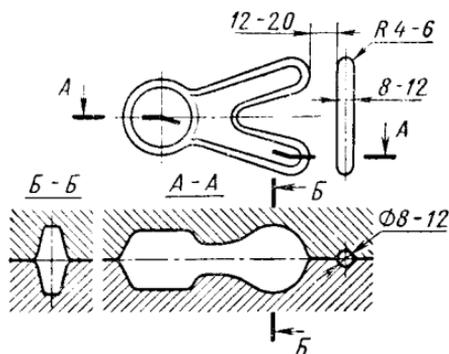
Канавка для торможения заусенца у предварительного ручья
